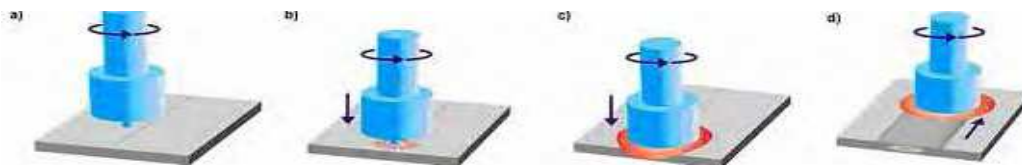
Etapes du procédé de soudage par frottement et malaxage (FSW)
